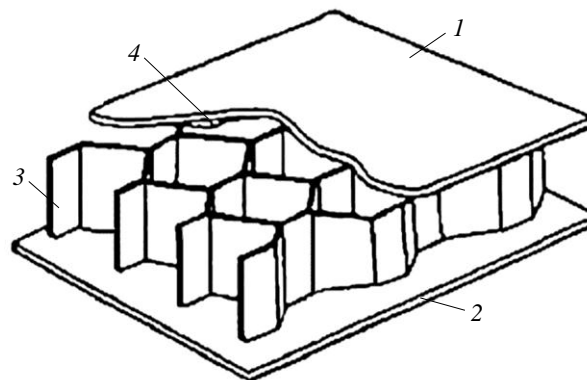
Состав трехслойной сотовой панели: 1 – обшивка; 2 – клеевая пленка; 3 – сотовый наполнитель; 4 – полимерный наполнитель (сферопласт)
